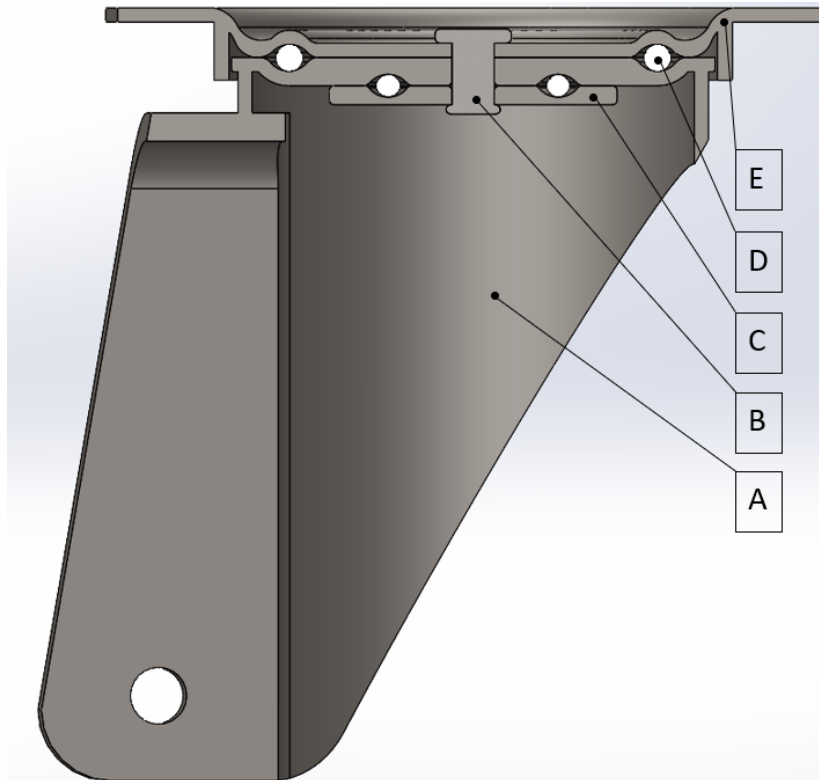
Modelação em ambiente SolidWorks – Estrutura metálica da roda – Vista em corte
